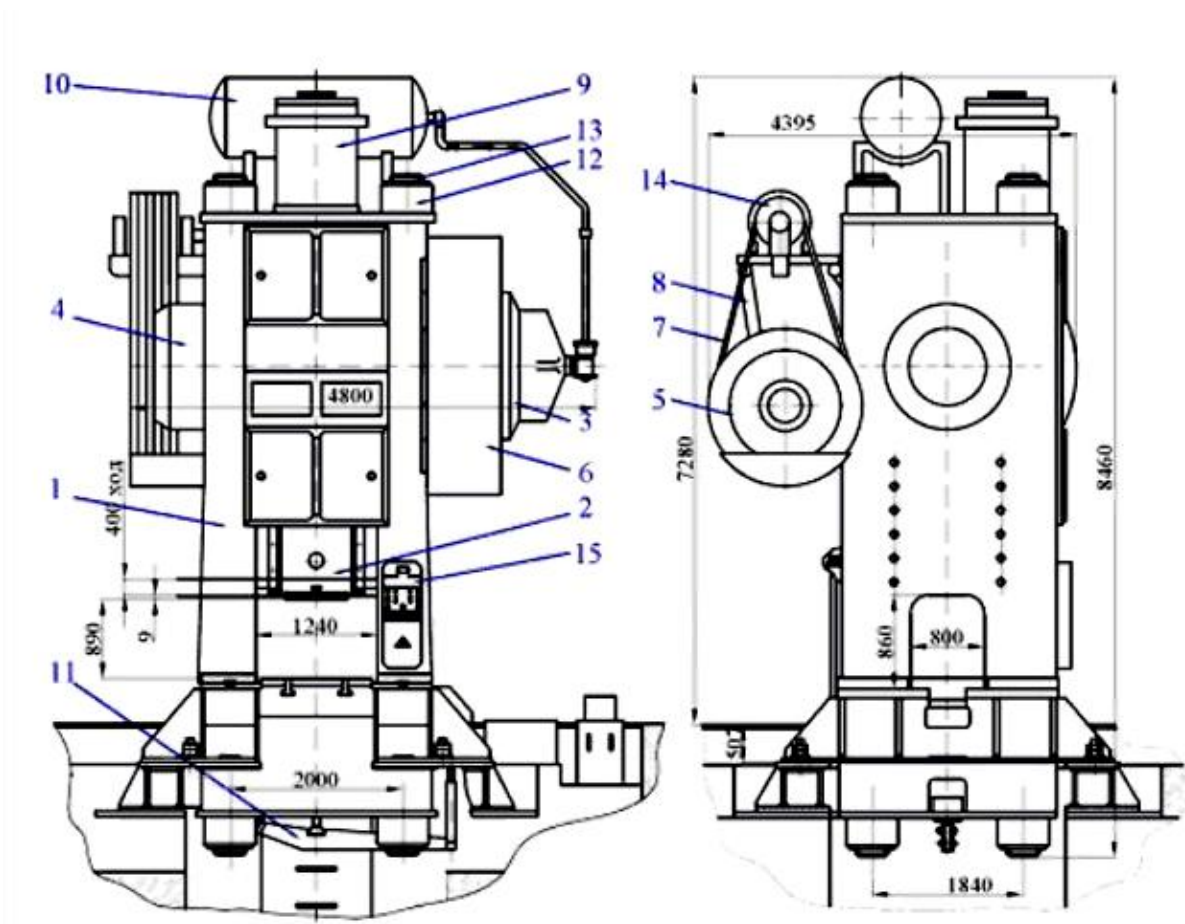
Загальний вид КГШП зусиллям 25 МН: 1 – станина, 2 – повзун, 3 – муфта, 4 – гальма, 5 – маховик, 6 – кожух зубчастого колеса, 7 – клинопасова передача, 8 – пристрій для натягування пасів, 9 – врівноважувач, 10 – ресивер, 11 – виштовхувач, 12 – гайка, 13 – стяжна шпилька, 14 – головний електродвигун, 15 – пульт керування.
